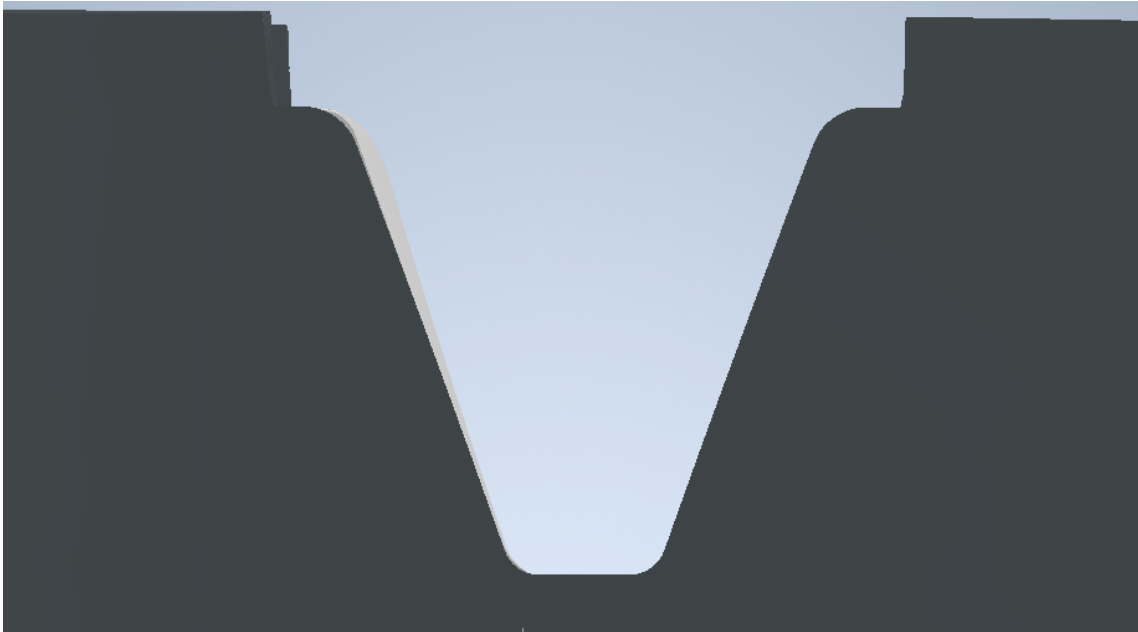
Sovrapposizione dei profili vista petto tagliente.
